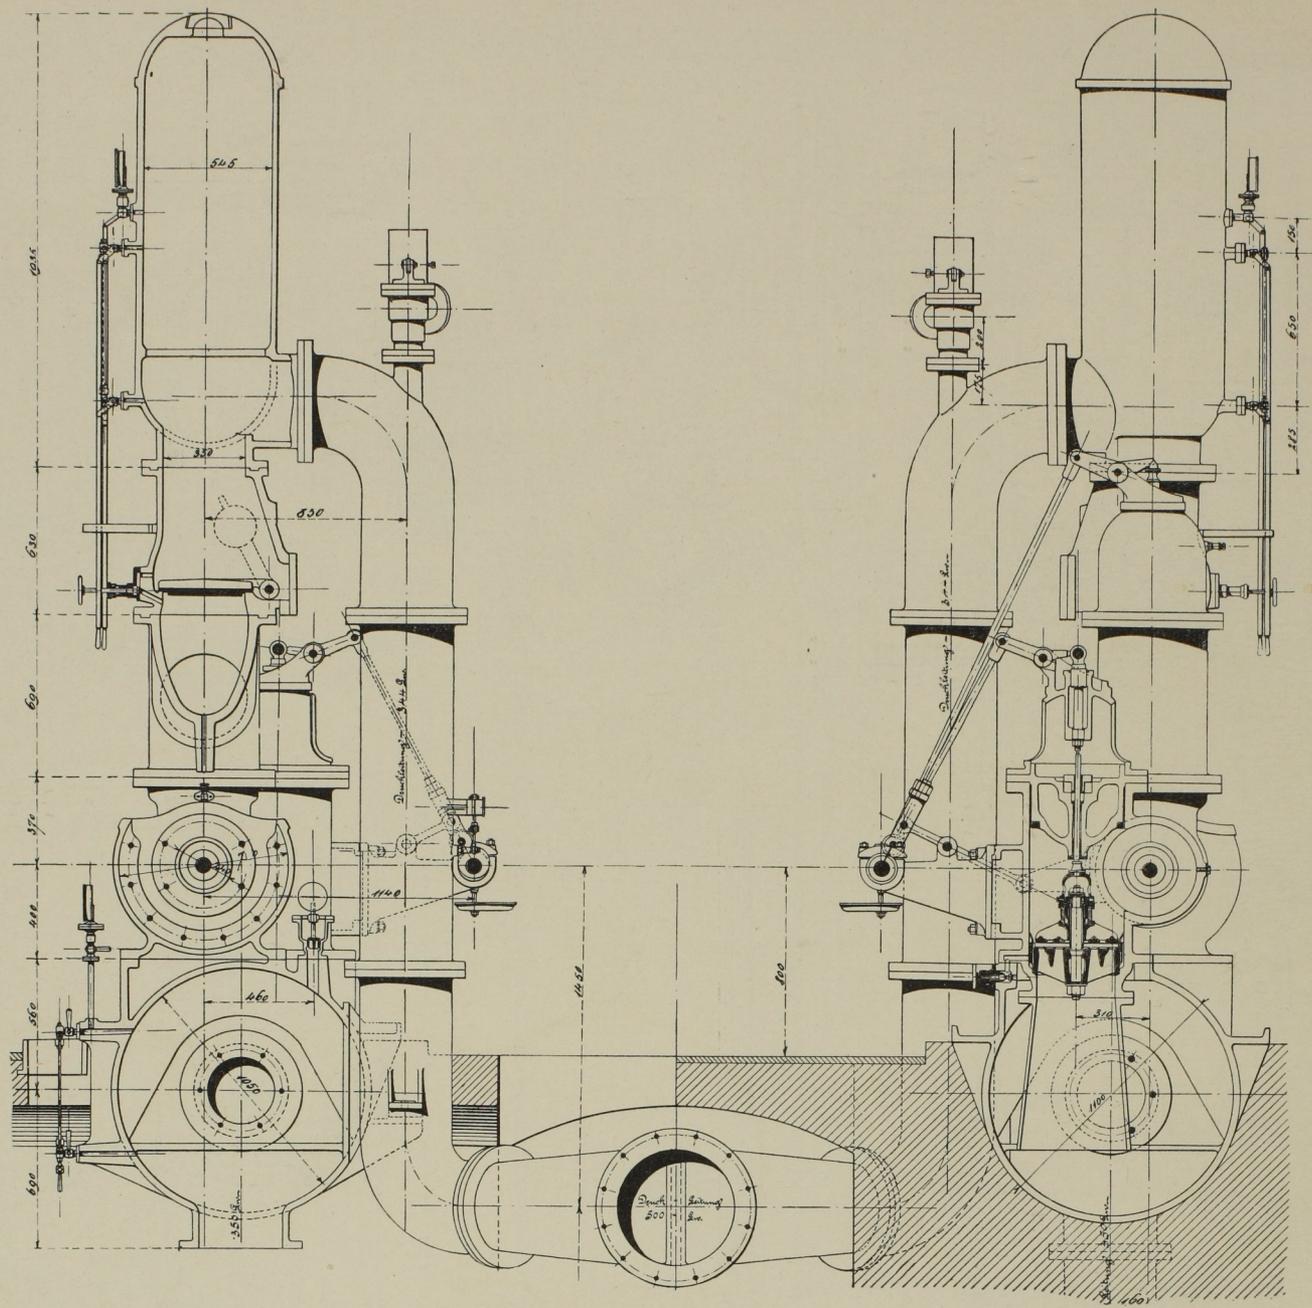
Querschnitt der Druckpumpen und Pumpensteuerung. Masst. 1:30.
